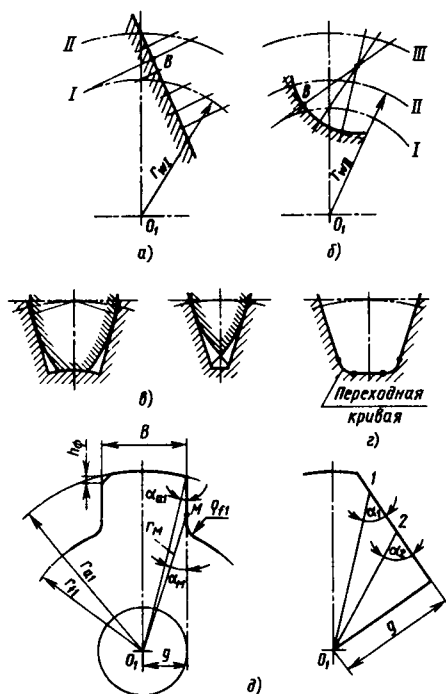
Условия обработки профиля заготовки и размеры прямолинейного профиля детали
